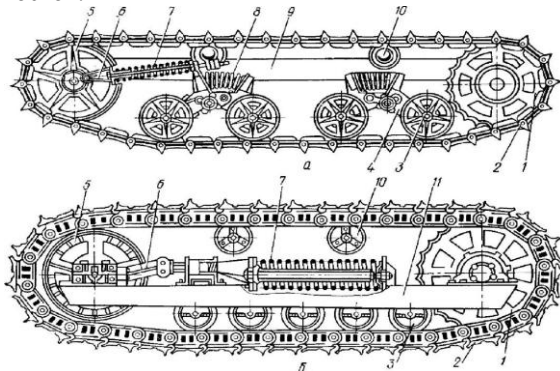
Конструкції пружної (*а*) і напівтвердої (*б*) підвісок гусеничних тракторів: 1 - ведуча зірочка; 2 - гусениця; 3 - опорний коток; 4 - каретка; 5 - напрямне колесо; 6 - натягувальний пристрій; 7 - пружина; 8 - амортизатор каретки; 9 - озов трактора; 10 - підтримувальний ролик; 11 - гусеничний візок.
